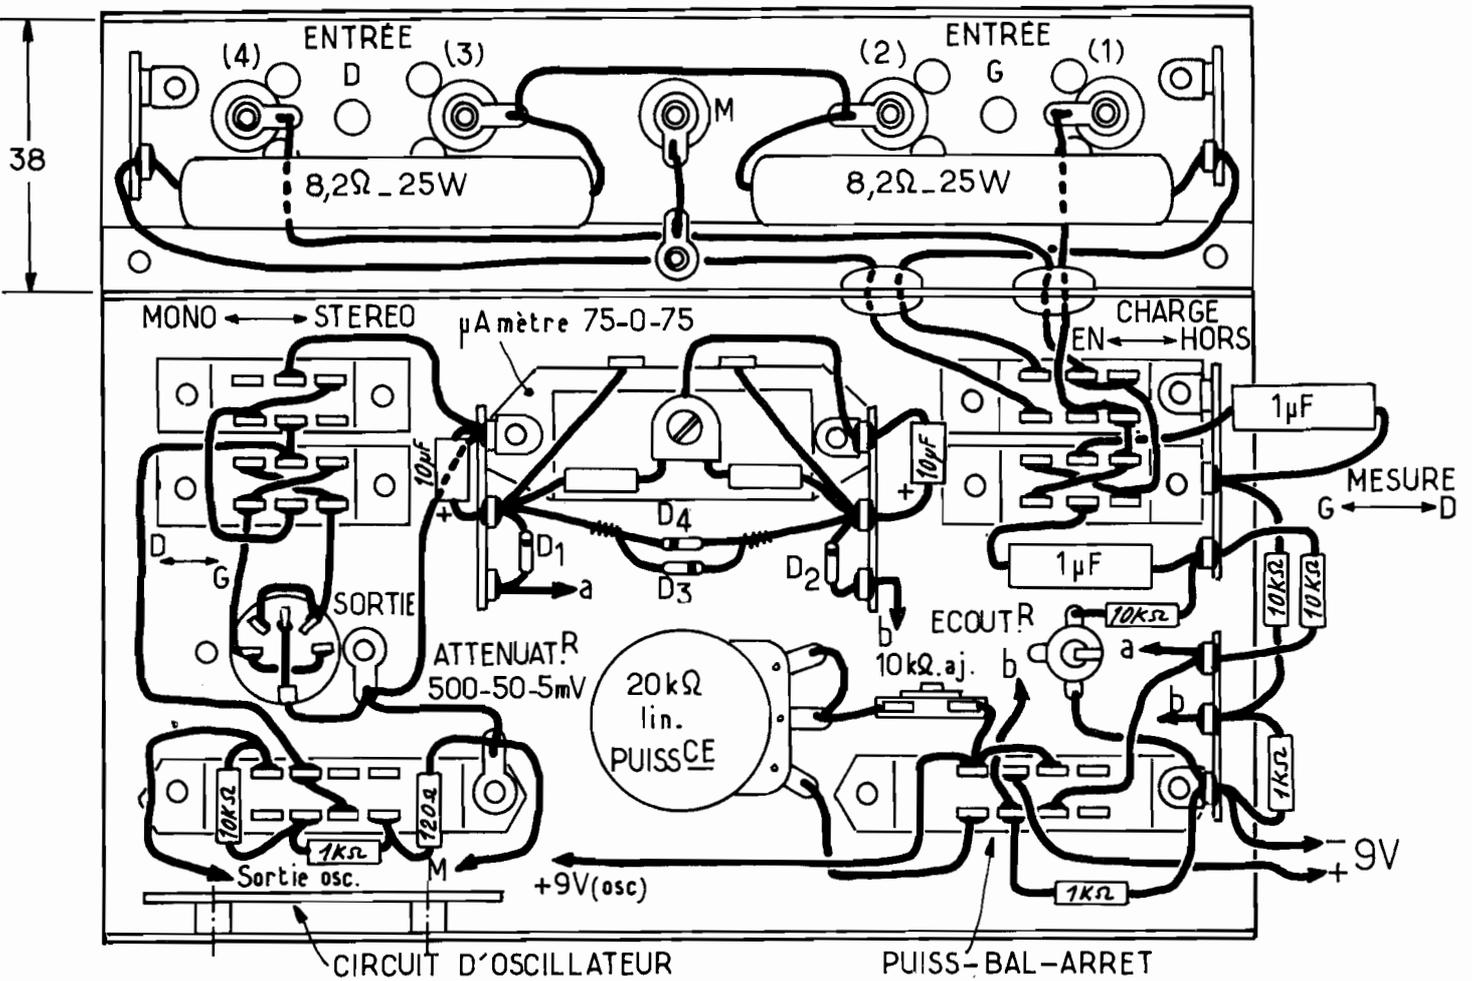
Plan de câblage et dimensions du Hi-Fi tester.
